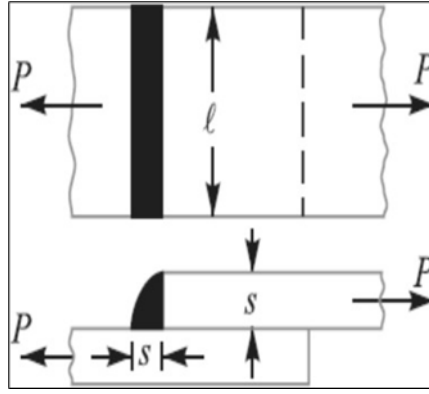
सिंगल ट्रान्सव्हर्स फिलेट (Single transverse fillet weld)
